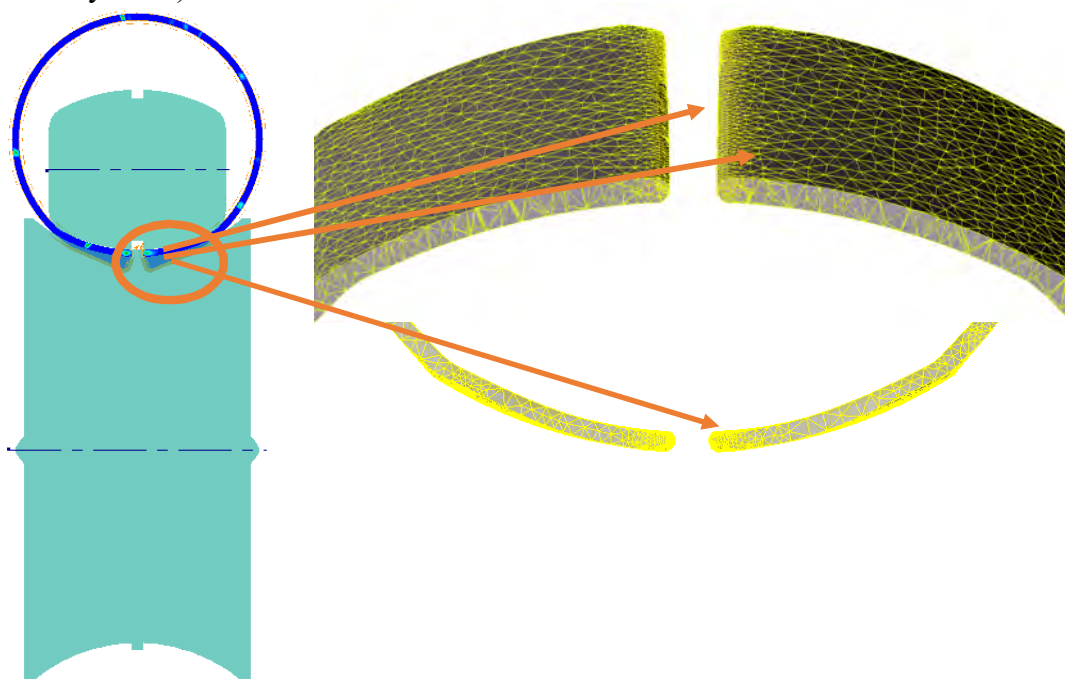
Общий вид инструмента и заготовки при процессе догибки кромок, потеря толщины металла в зоне кромок
